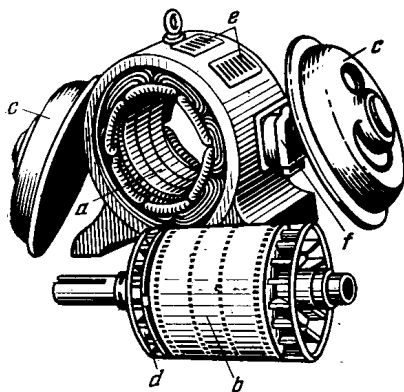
Moteur asynchrone à rotor en court-circuit démonté:
